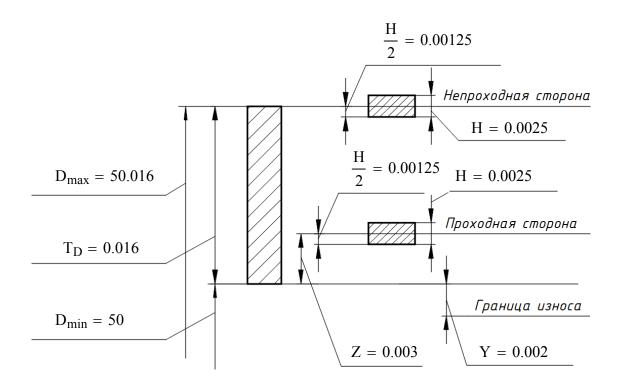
Схема расположения полей допусков калибра-пробки
